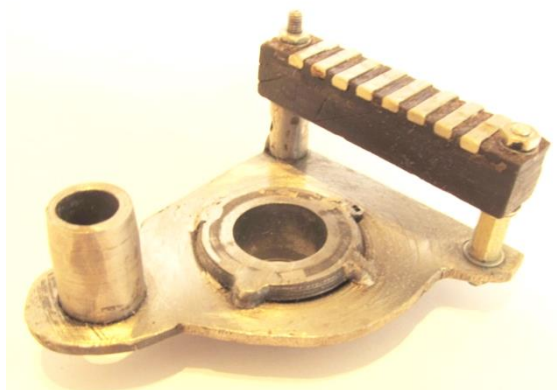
Деталі струмоз’ємного пристрою
